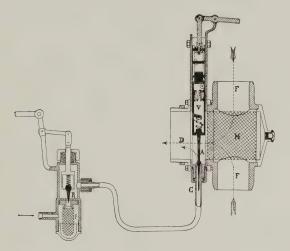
Carburateur « Blocktube » système Tampier pour rotatif.
